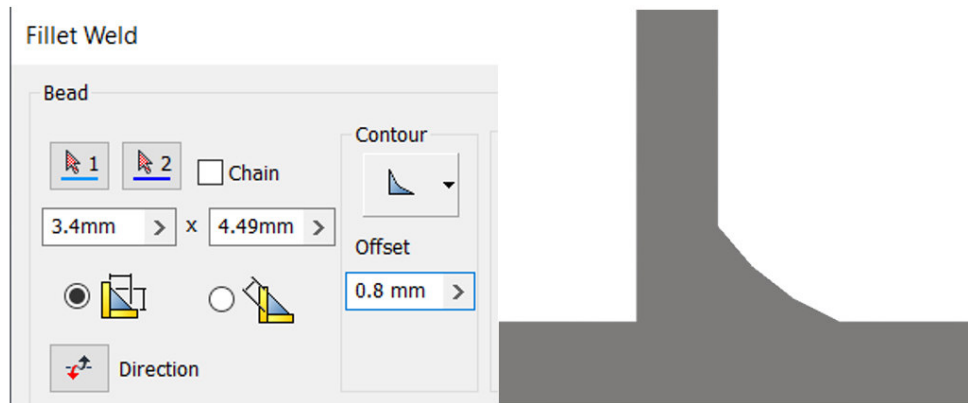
Dimensionamiento del cordón de soldadura y vista lateral ampliada del cordón obtenido.
